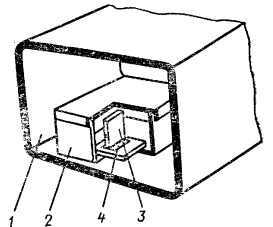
Схема пайки с применением защитного экрана: 1 — герметичный контейнер; 2 — защитный экран; 3 — паяльный образец; 4 — припой
